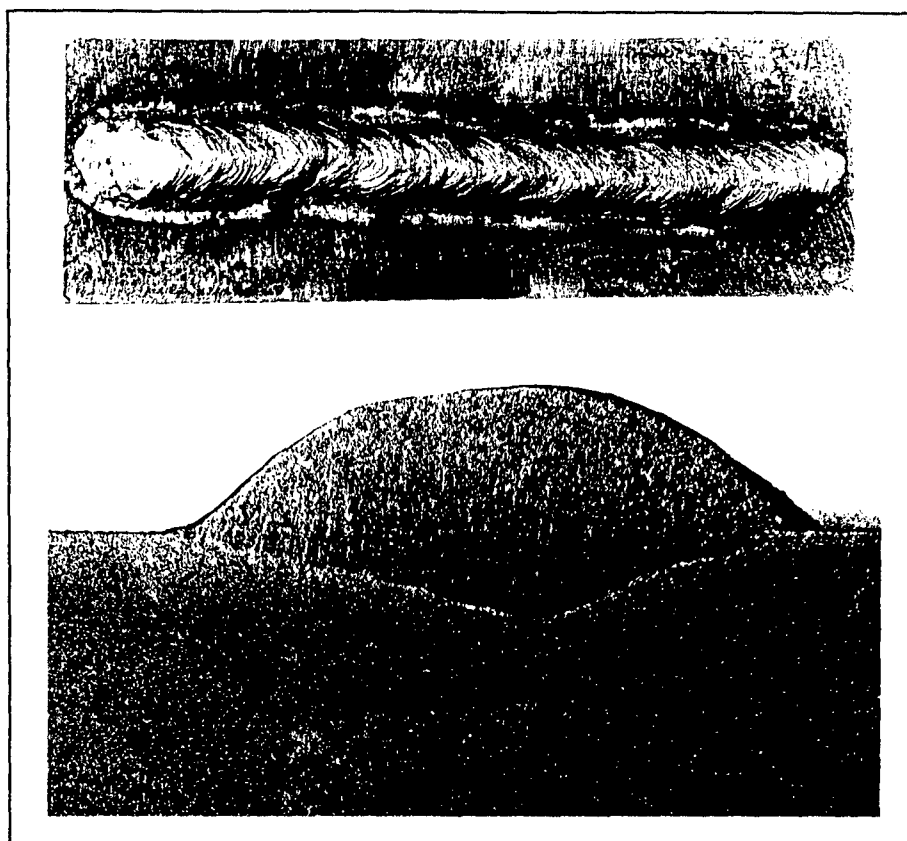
Aspecto do cordão de solda para o eletrodo E em CC+.
